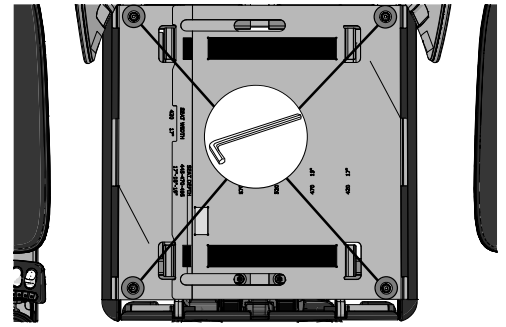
Die Sitzplatten werden von vier Schrauben gehalten.
